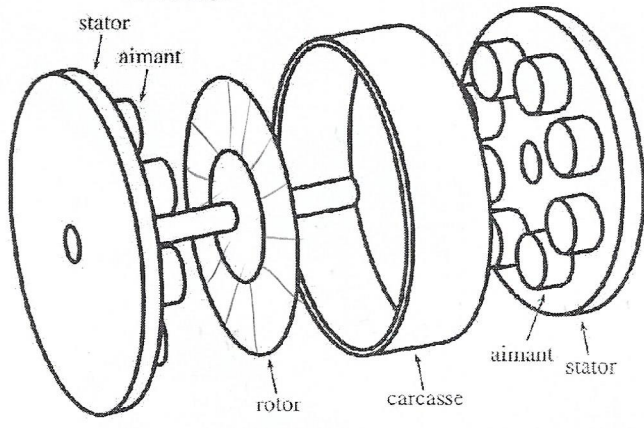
Vue éclatée d'une MCC à entrefer plan.
